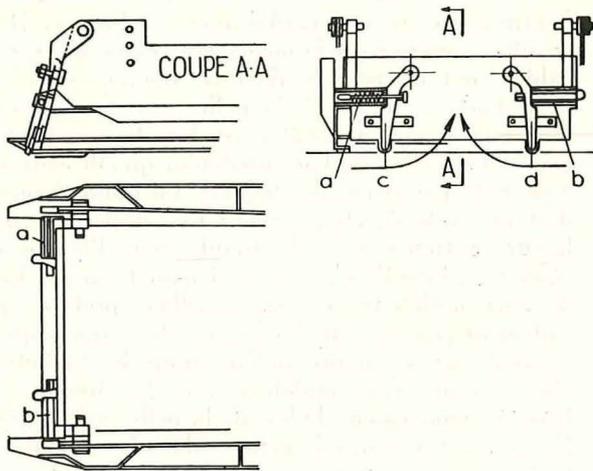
Coupe, élévation et vue en plan de la porte avec son verrouillage.
